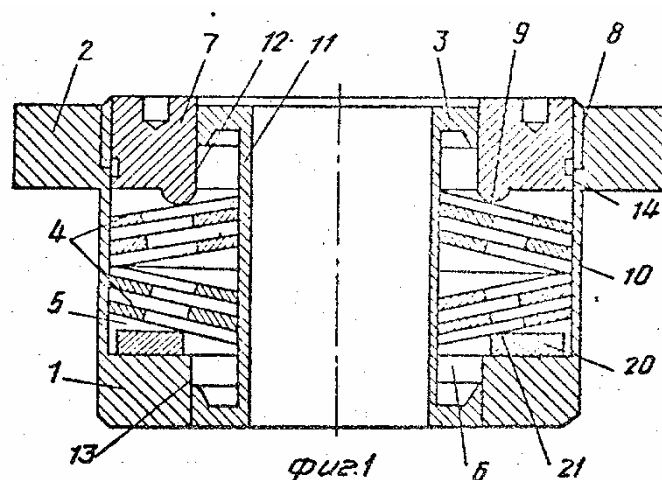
Кондукторная втулка (патент SU1328085)
